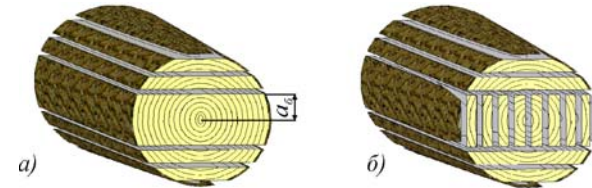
Схема розпилювання колод брусо-розвальним способом з формою поперечного перетину у вигляді еліпса:
